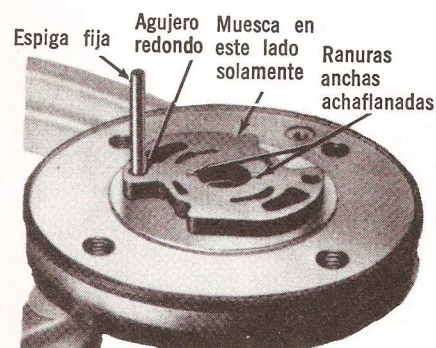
Placa Inferior de Presión Instalada. Típico
